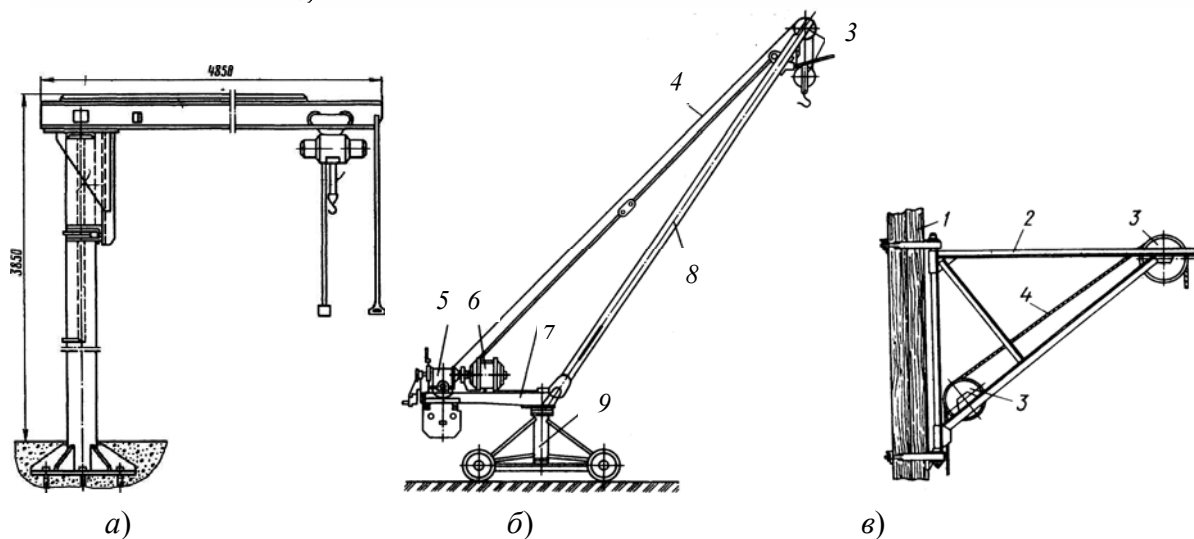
Консольно-поворотные краны: а – напольный; б – полноповоротный передвижной; в – настенный (кран-укосина): 1 – строительная конструкция; 2 – несущая ферма; 3 – блоки; 4 – канат; 5 – червячный редуктор; 6 – электродвигатель; 7 – платформа; 8 – стрела; 9 – тележка
